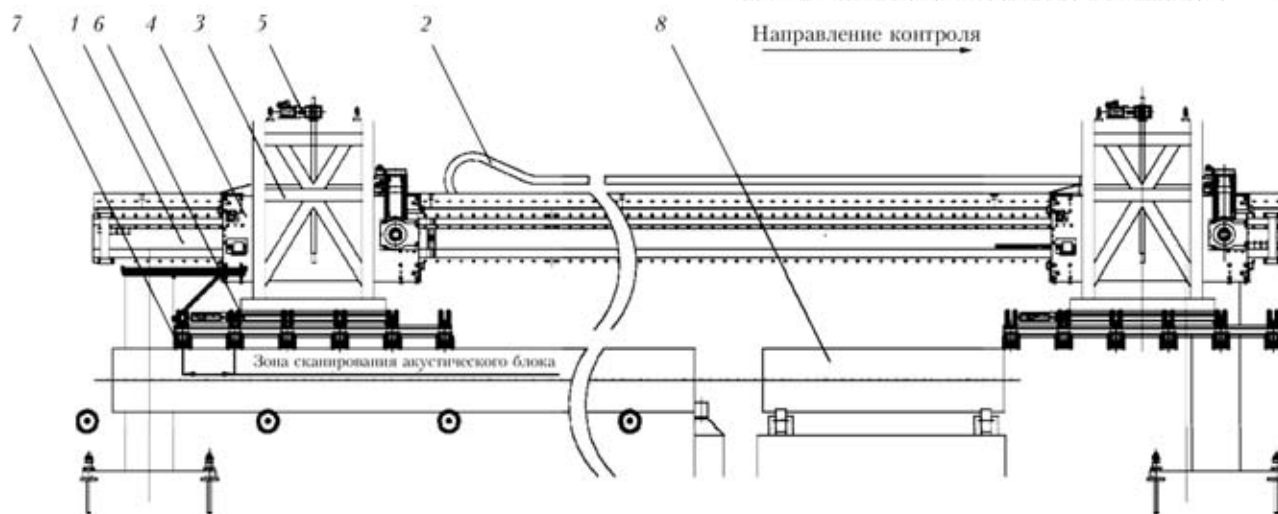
Установка НК 380ВЛ для АУЗК тела труб: 1 — продольная балка с ходовой зубчатой рейкой длиной 19 м; 2 — гибкий канал для укладки электрокабелей, гидро- и пневмошлангов; 3 — траверса вертикального перемещения акустических блоков; 4 — механизм горизонтального продольного перемещения вдоль трубы; 5 — механизм вертикального перемещения с электроприводом; 6 — модуль сканирования акустических блоков; 7 — акустический блок; 8 — стандартный образец на позиции калибровки
